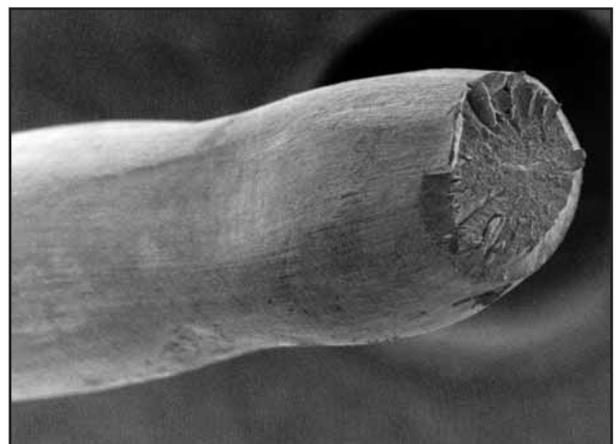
Dieser Draht bildete vor dem Bruch zunächst an zwei benachbarten Stellen Brucheinschnürungen aus.
